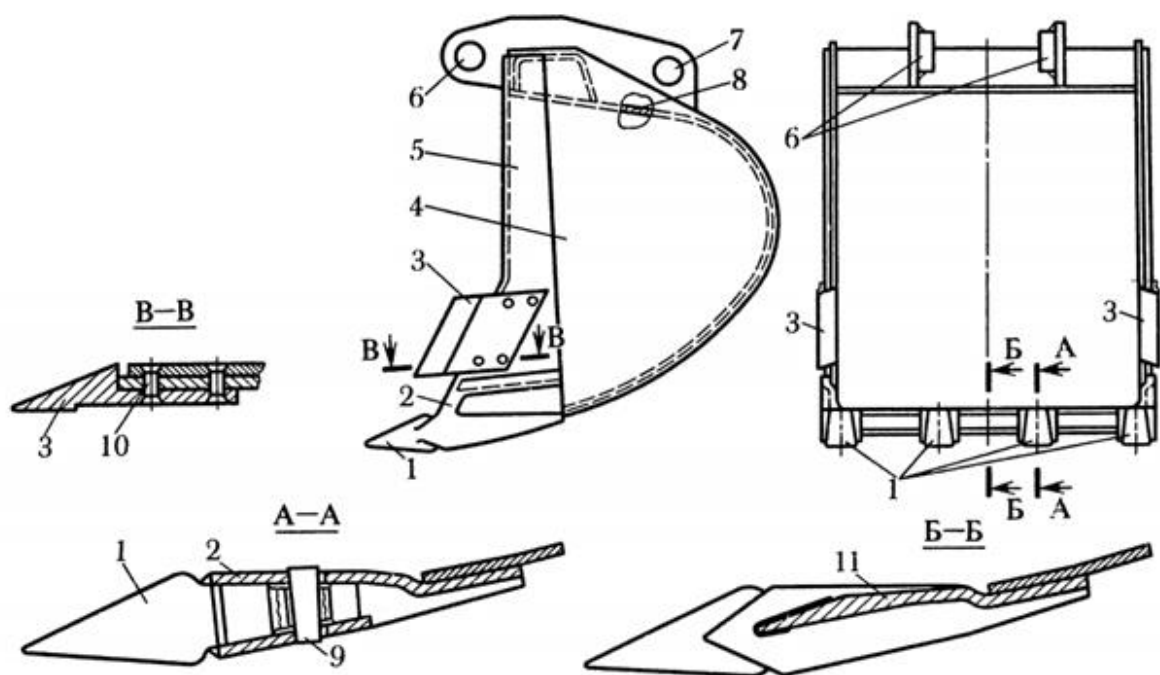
Ковш обратной лопаты экскаватора ЭО-3322А
